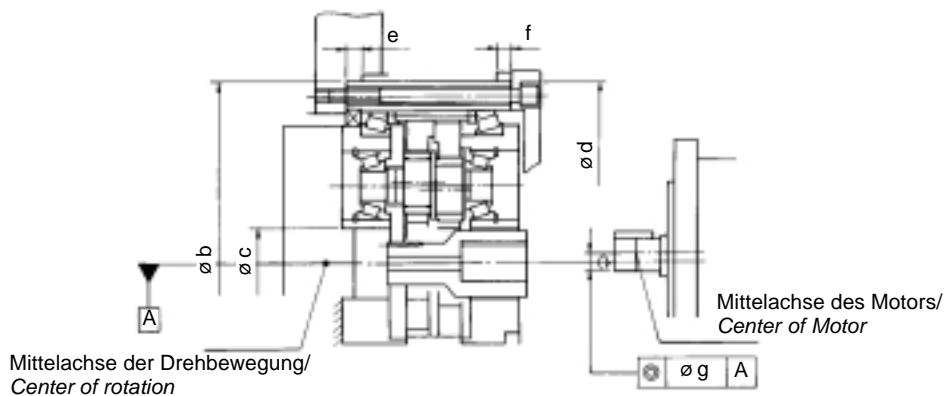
Einbautoleranzen/Assembly tolerance
